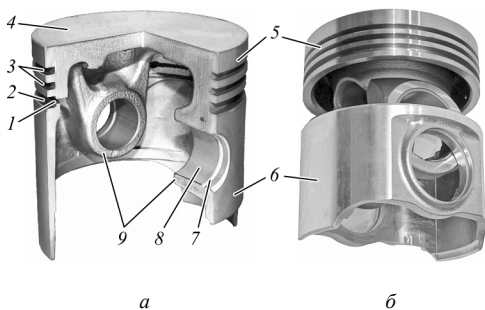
Поршень: а – цельный; б – составной; 1 – отверстия для слива масла; 2 – канавка под маслоъемное кольцо; 3 – канавка под компрессионное кольцо; 4 – днище; 5 – головка; 6 – юбка; 7 – канавка под стопорное кольцо; 8 – отверстие под поршневой палец; 9 – бобышка
